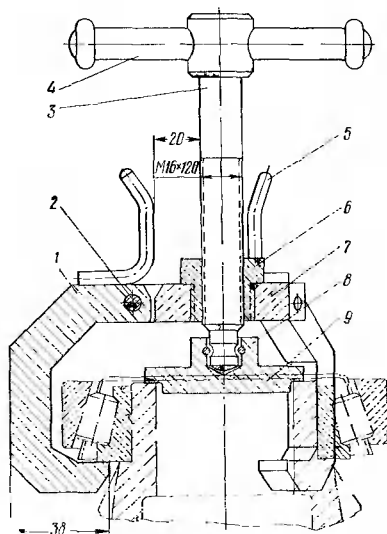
Съемник подшипника с левой чашки дифференциала заднего моста:
